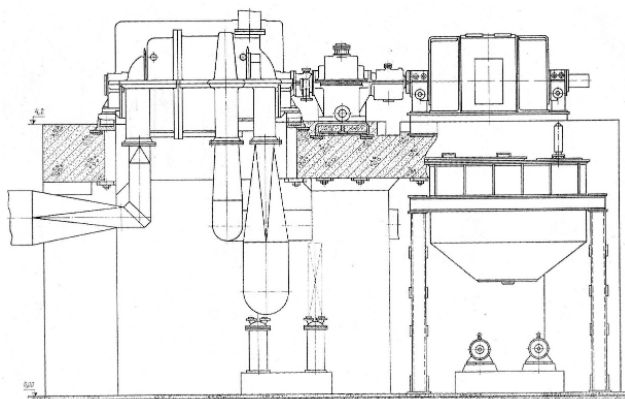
Нагнетатель (слева) в составе турбокомпрессорного агрегата
